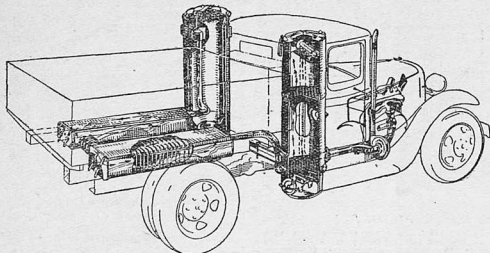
Расположение агрегатов газогенераторной установки НАТИ Г-14 на шасси автомобиля
